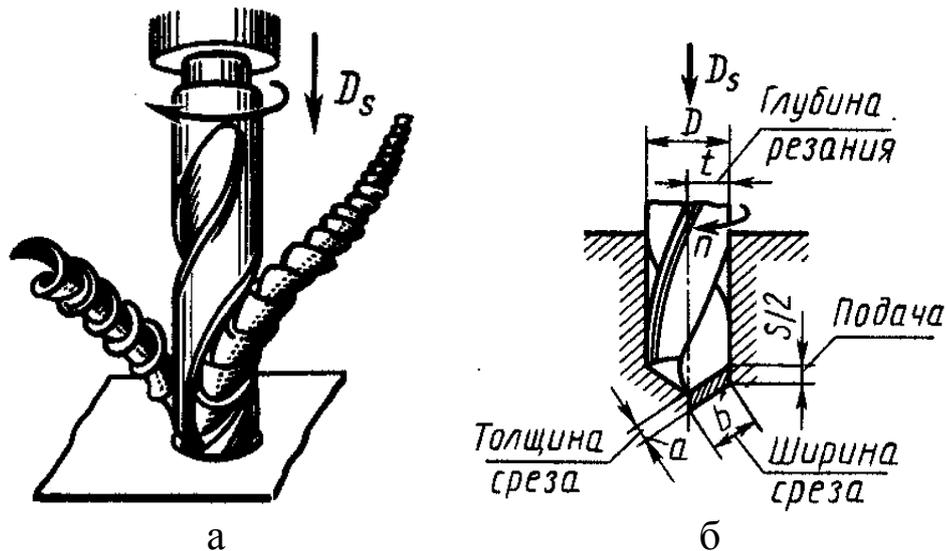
Процесс сверления: а - движение инструмента при сверлении; б - элементы резания
